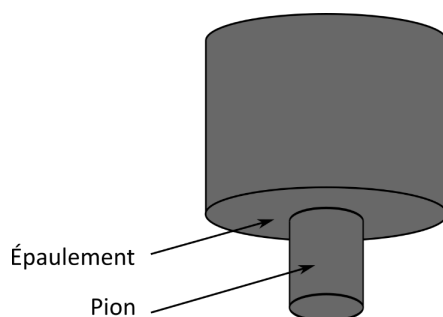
Schéma d'un outil utilisé pour le Friction Stir Welding-Processing
